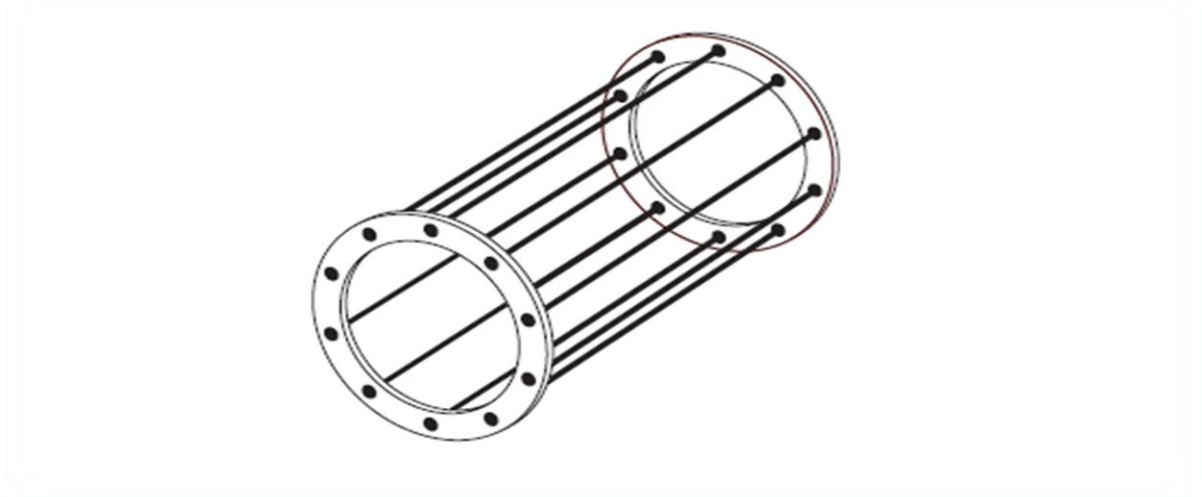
Conducteur du rotor en cage d'écureuil [1]
